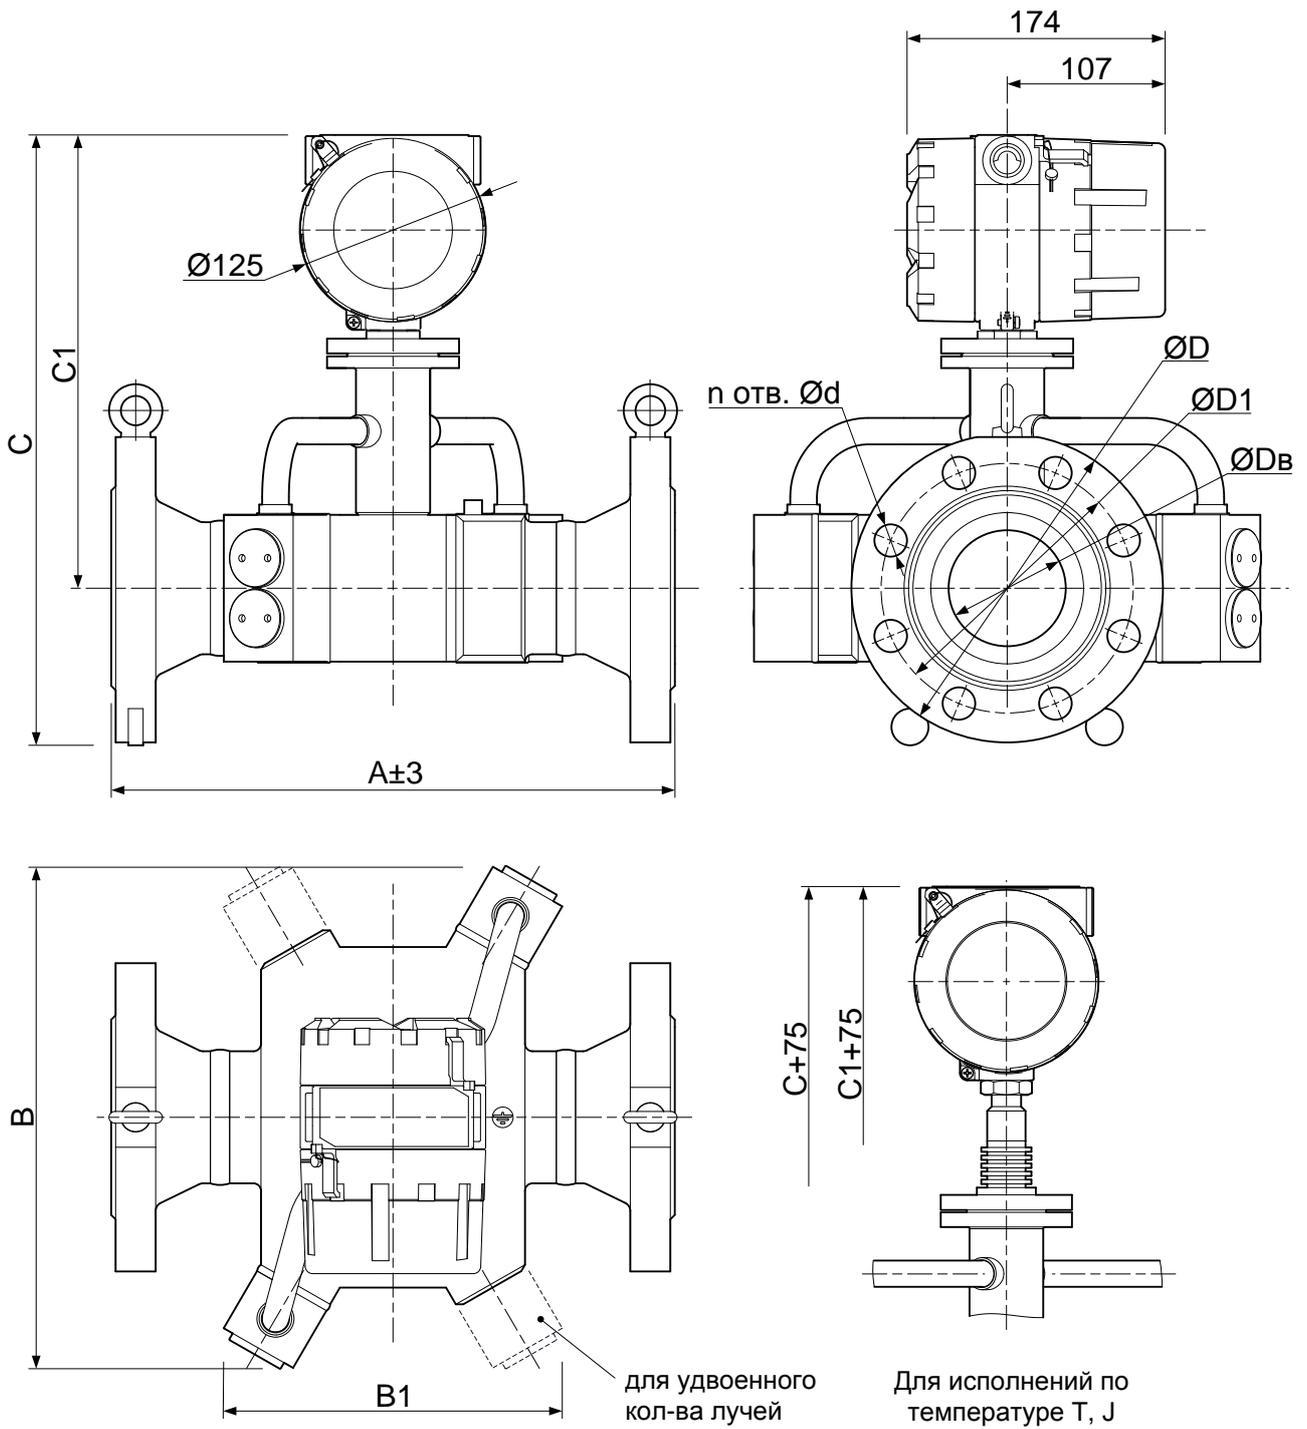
Габаритные размеры датчиков с PN:
